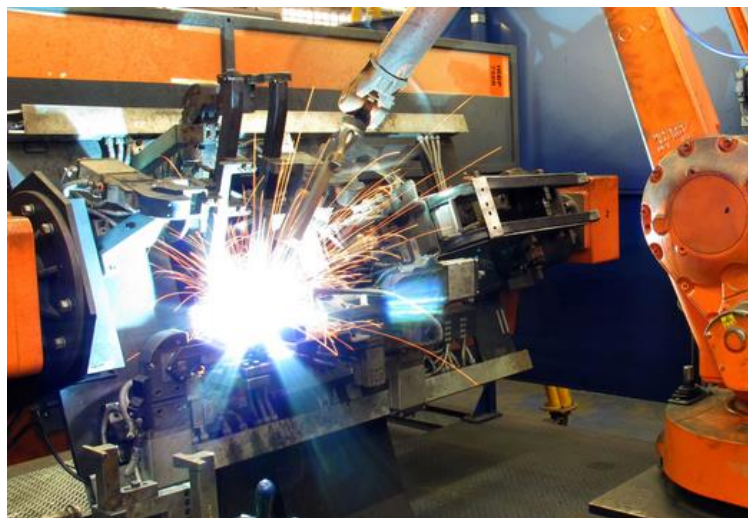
Robô soldadura tubos TRW ABB IRB1600-IRC5-M24004
